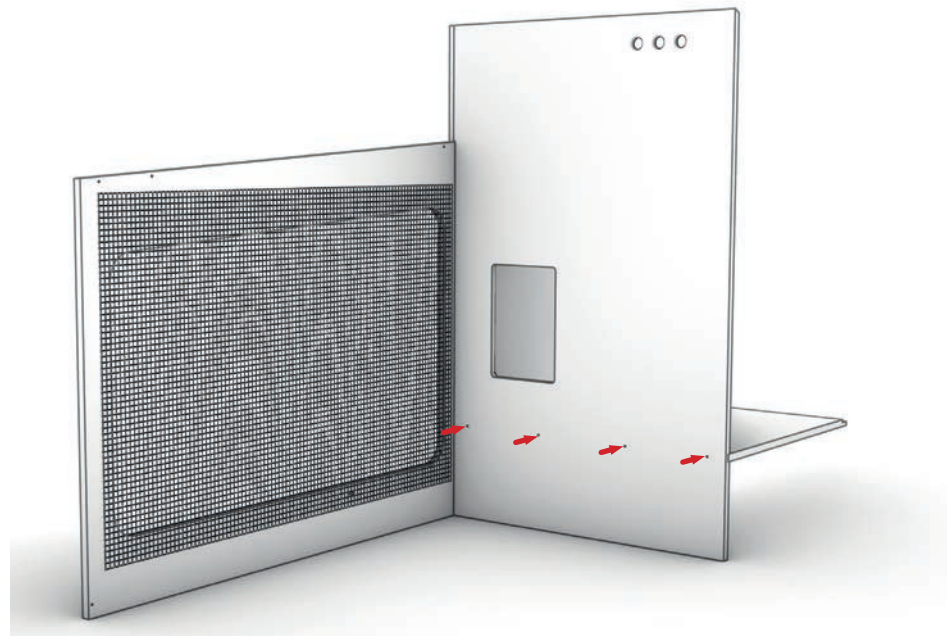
Frontplatte mit Bodenplatte verschrauben
